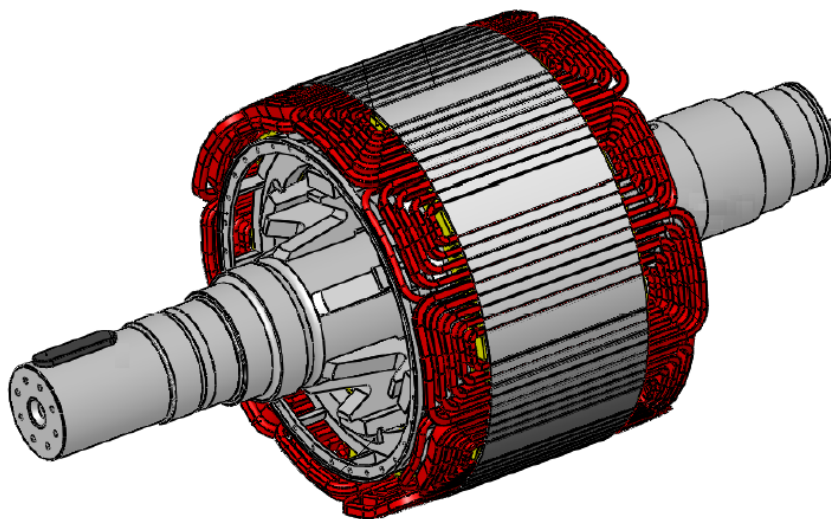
Vista do rotor bobinado da MATRBGC.
